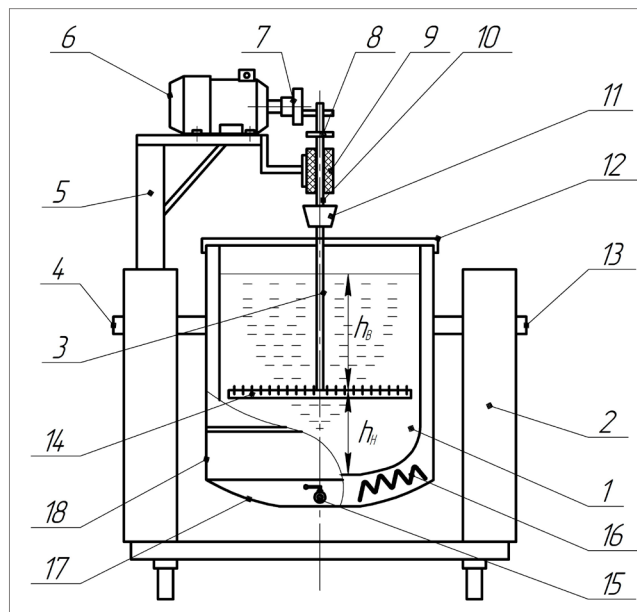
Схема установки: 1 – варочный сосуд; 2 – станина; 3 – шток; 4 – цапфа левая; 5 – опора электродвигателя привода; 6 – привод; 7 – планшайба сменная; 8 – ограничитель сменный; 9 – подшипник скольжения; 10 – водило; 11 – разъем конический; 12 – крышка съемная; 13 – цапфа правая; 14 – тарелка вибрационная; 15 – кран сливной; 16 – трубчатый электронагреватель (ТЭН); 17 – дно съемное; 18 – котел наружный.
